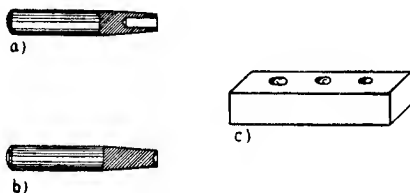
Nietwerkzeuge; Nietzieher (a), Nietkopfschneider (b) und Gegenhalter (c) zum Einspannen in den Schraubstak
